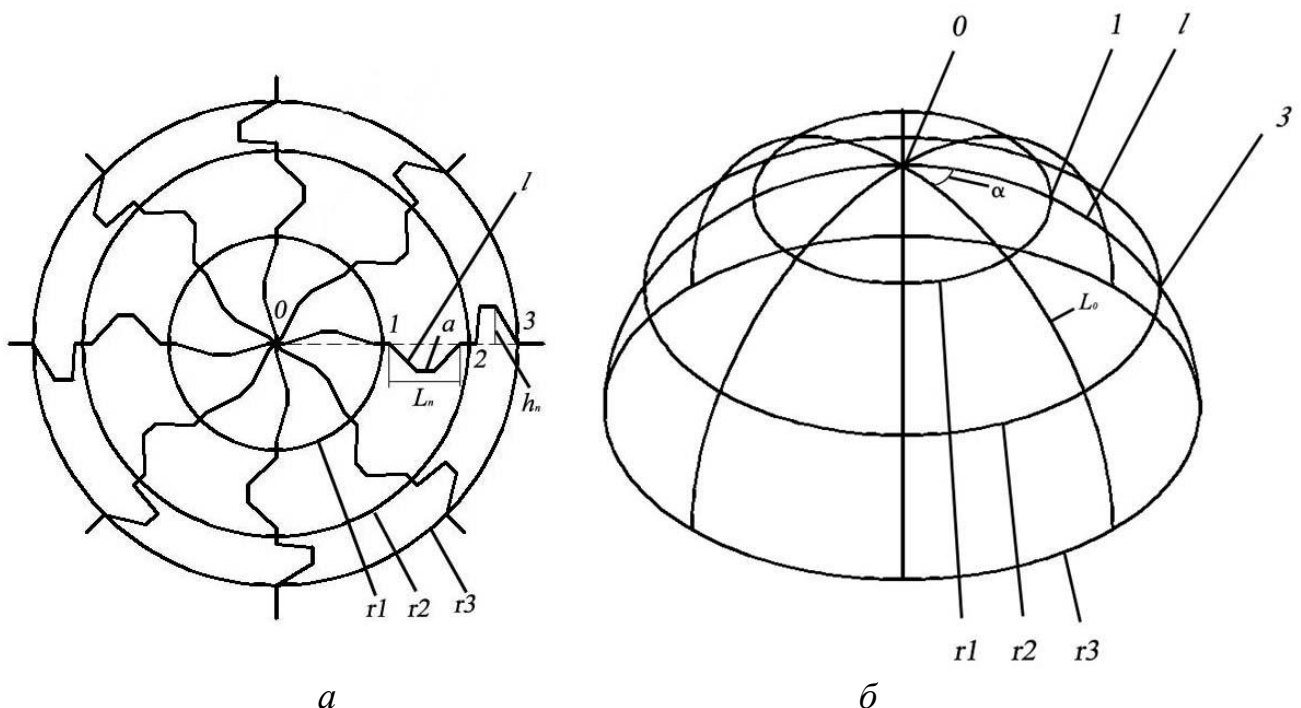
Структура полусферической оболочки: а - двумерная форма; б - трехмерная форма
